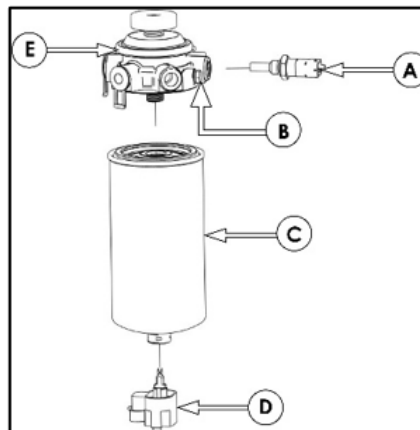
VUE ÉCLATÉE DU FILTRE À CARBURANT
